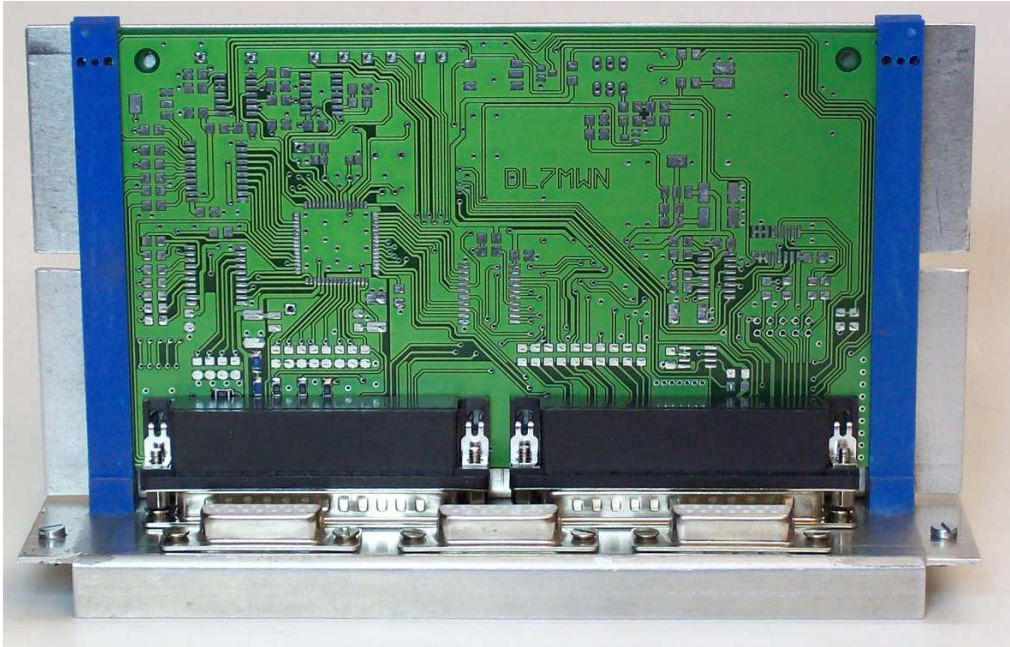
Montageblech 1 mit eingeschobenem, unbestücktem Steuerrechner
